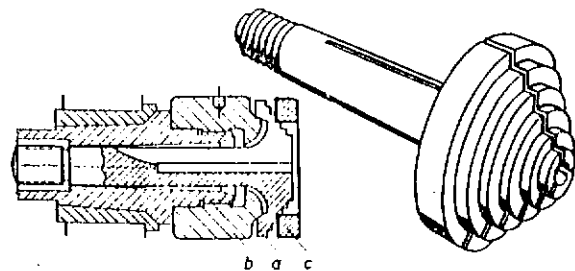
Sujeción en el plato escalonado exteriormente: a) plato escalonado exteriormente; b) plato de base; c) pieza.
